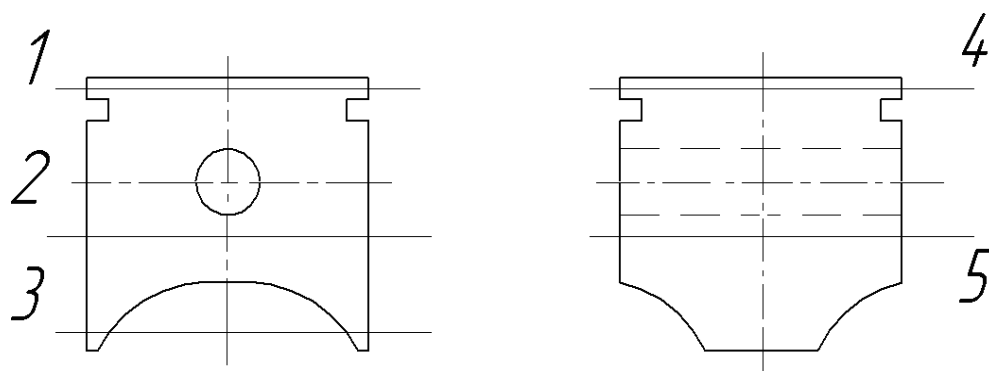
Схема розташування контрольних точок на поверхні поршня.
